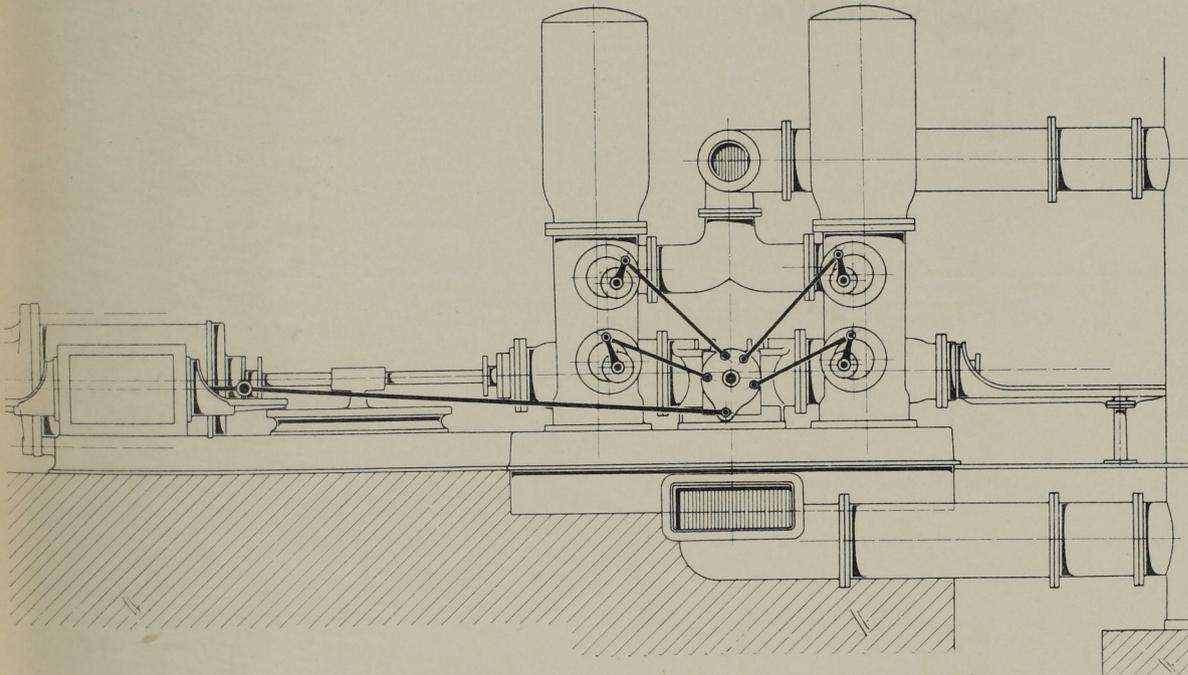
Pumpmaschine für Fontänenbetrieb. Seitenansicht. Massst. 1:50.
